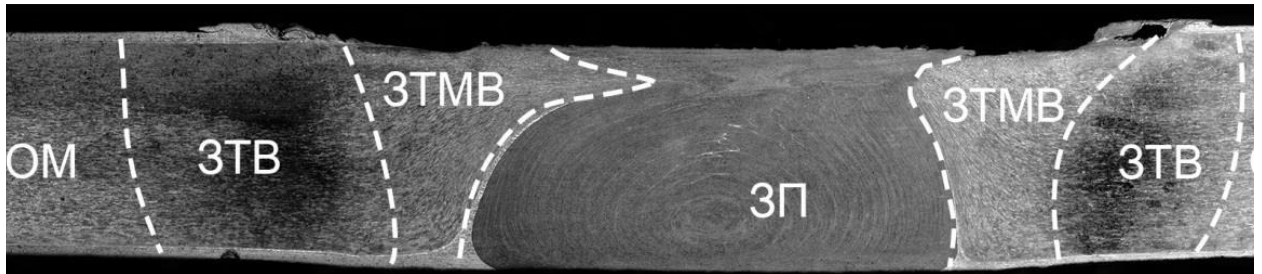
Схема расположения зон в сварном соединении сплава системы Al–Cu–Mg:
